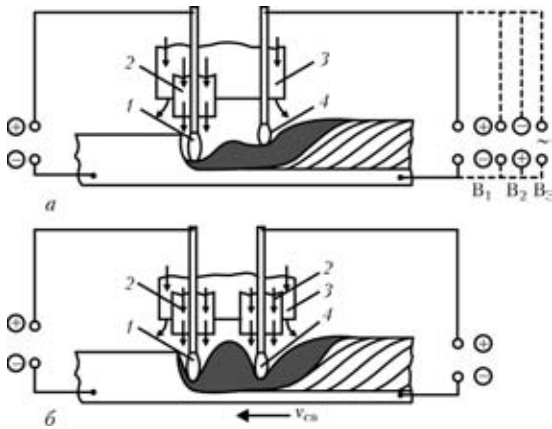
Схема двухдуговой сварки с двухскоростной газовой защитой одной (а) и двух (б) дуг: 1, 4 — соответственно первая и вторая дуга; 2 — сопло для подачи высокоскоростного потока газа; 3 — сопло для подачи защитного газа с обычной скоростью
